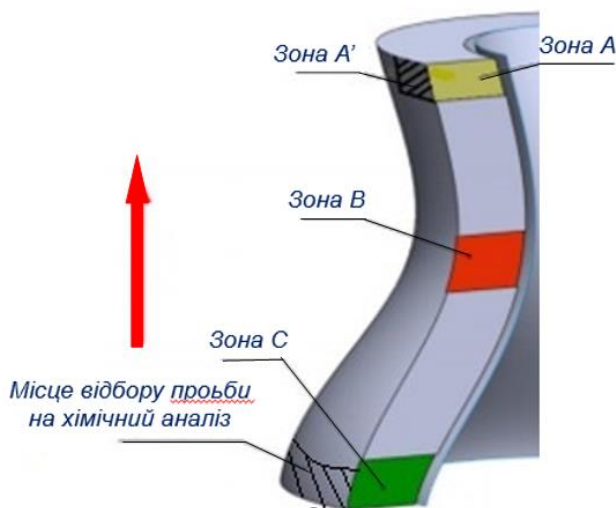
Зовнішній вигляд виробу зі сплаву Inconel 718 з розміткою вирізки заготовок під зразки для випробувань
